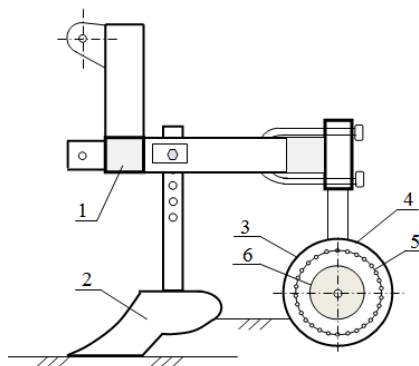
Схема окучника и прикатывающего катка для измельчения поверхностной корки грядок:
